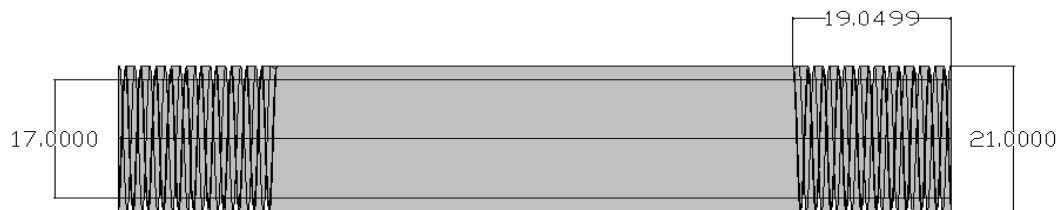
Dimensiones de rosca del ducto prefabricado.
